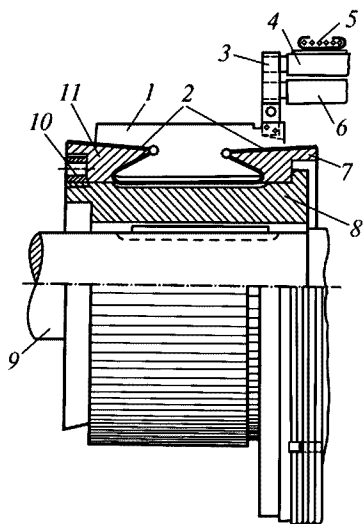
Устройство коллектора: 1 — коллекторная пластина; 2 — миканитовая манжета; 3 — «петушок» коллектора; 4, 6 — выводы секций обмотки якоря; 5 — бандаж; 7, 11 — стальные клинья; 8 — втулка; 9 — вал; 10 — гайка
